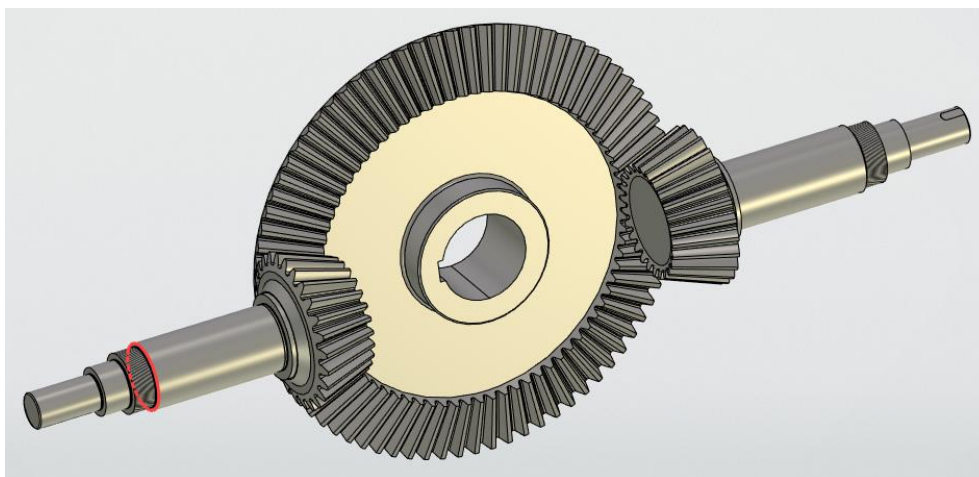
3D-модель конической шестерни (вид с двух сторон)
